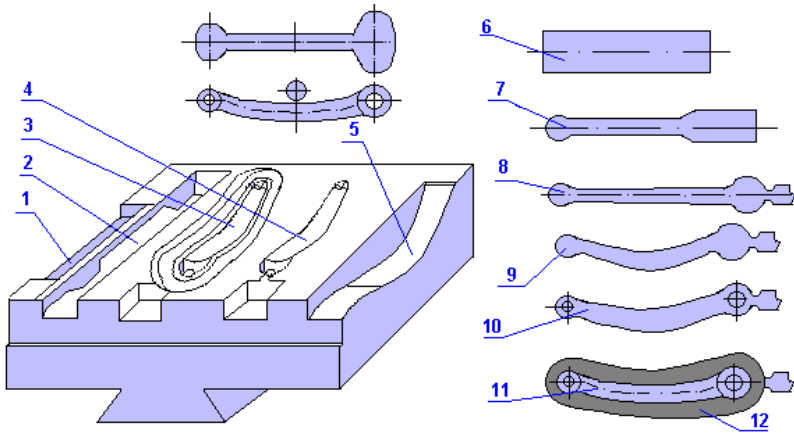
Стадії отримання складної поковки в декількох рівчаках. Позиція 6 – вихідна заготовка. Заготівельні рівчаки: 1 – протяжний рівчак (7 – поковка після протяжного рівчака); 2 – підкатний рівчак (8 – поковка після підкатного рівчака); 5 – згинальний рівчак (9 – поковка після оброблення в згинальному рівчаку). Штампувальні рівчаки: 4 – попередній (чорновий) струмок (10 – поковка після штампування в чорновому рівчаку); 3 – чистовий рівчак (11 – поковка після чистового рівчака)
